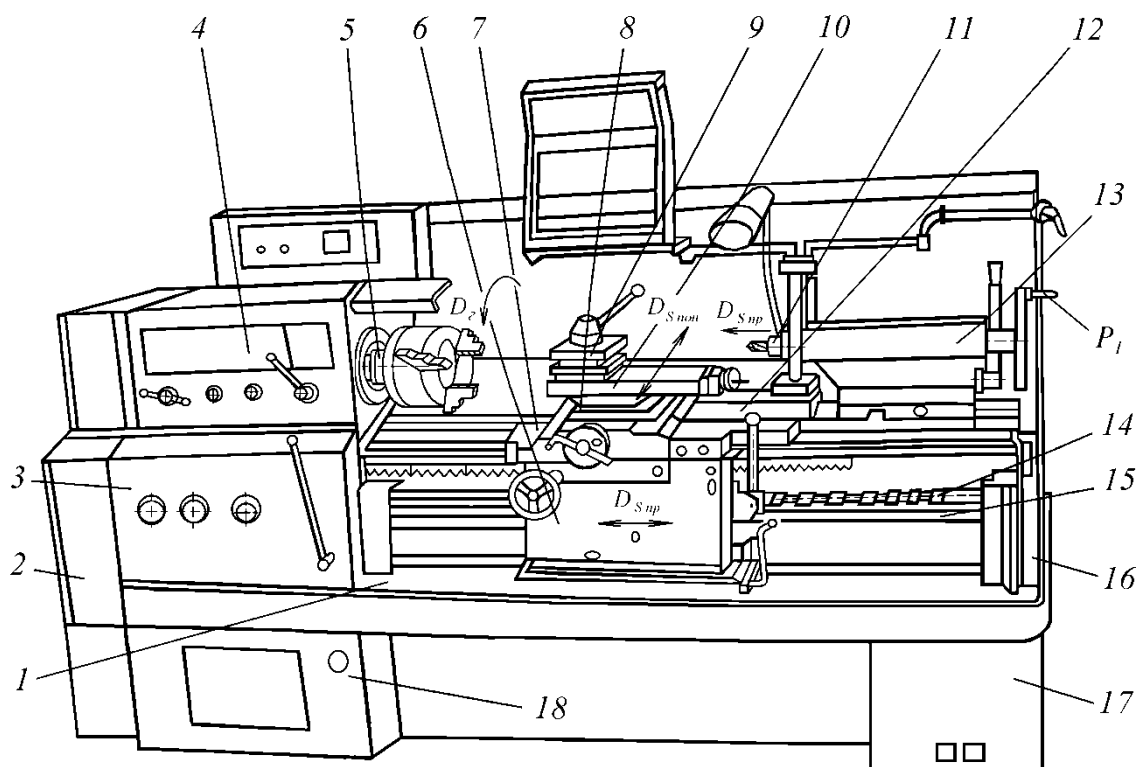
Общий вид токарно-винторезного станка модели 16К20
